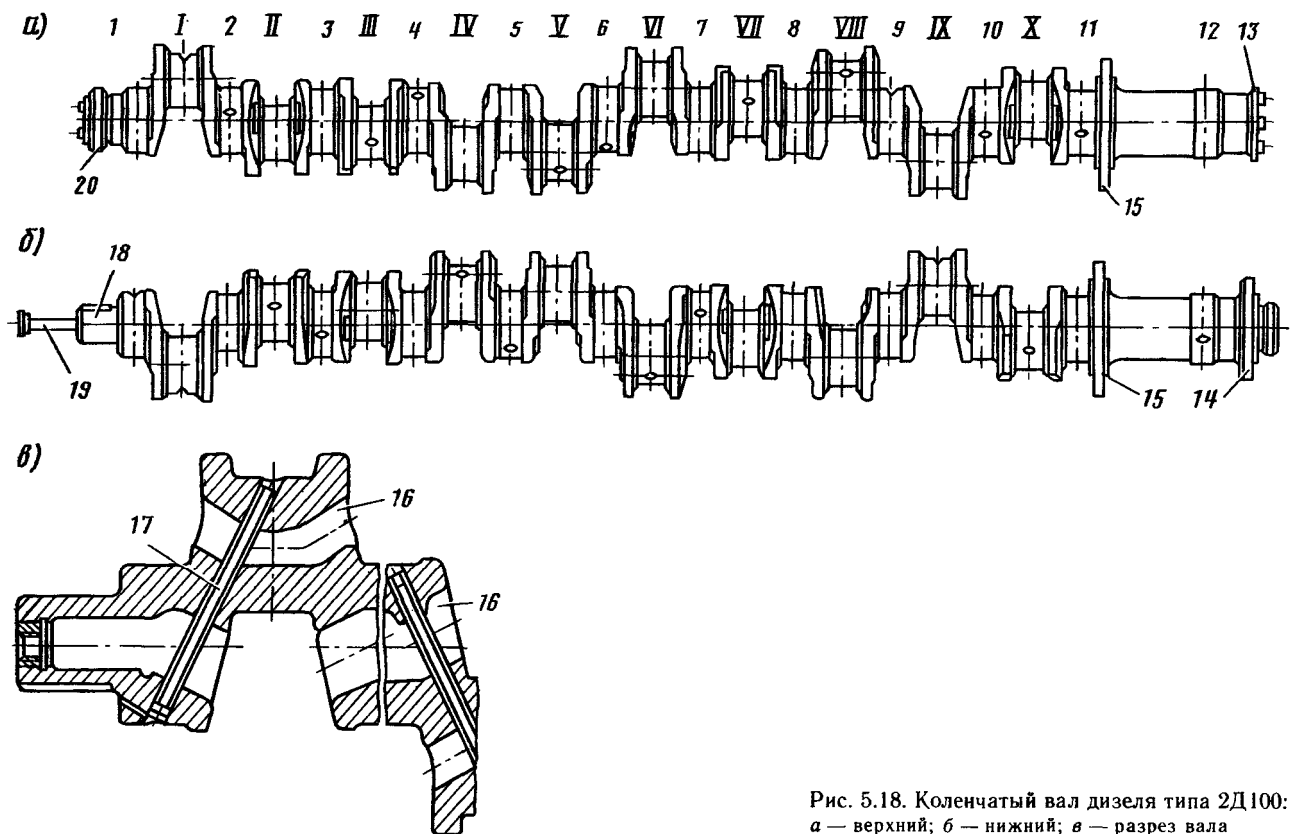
Коленчатый вал дизеля типа 2Д100:
